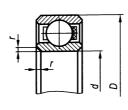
Подшипник шариковый радиальный однорядный гибкий
